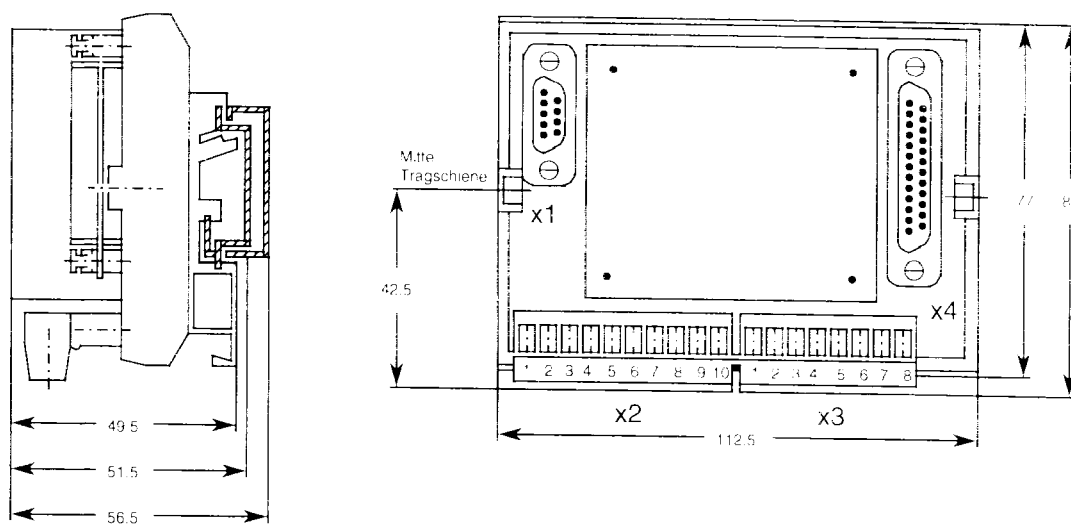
Габаритный чертеж, шинное задающее устройство SIPART, размеры в мм
